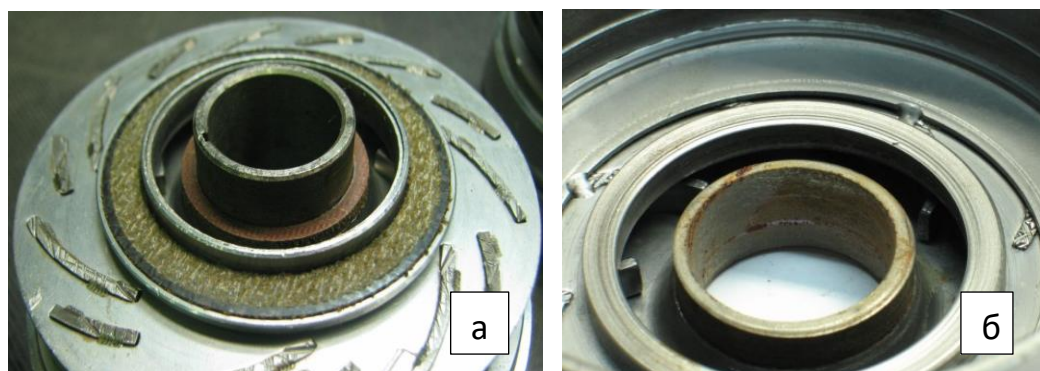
Общий вид РК – а, НА – б штамповарной конструкции (после опыта)
